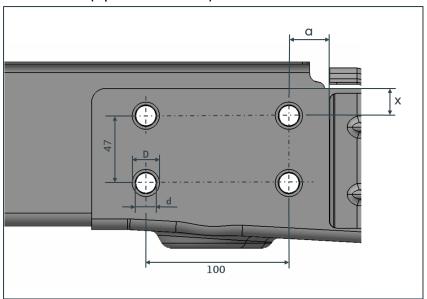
Fourgon-3,0 - 4,0 t (plancher bas)
